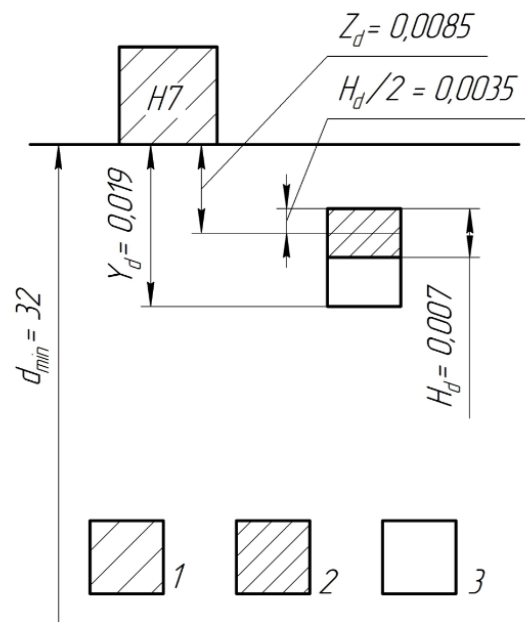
Схема расположения поля допуска центрирующего диаметра пробки:
